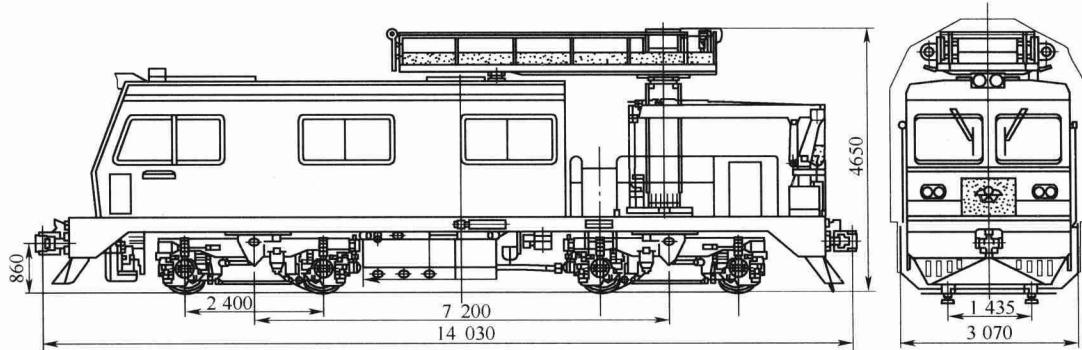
JW-4 型接触网作业车外形及平面布置(单位:mm)
